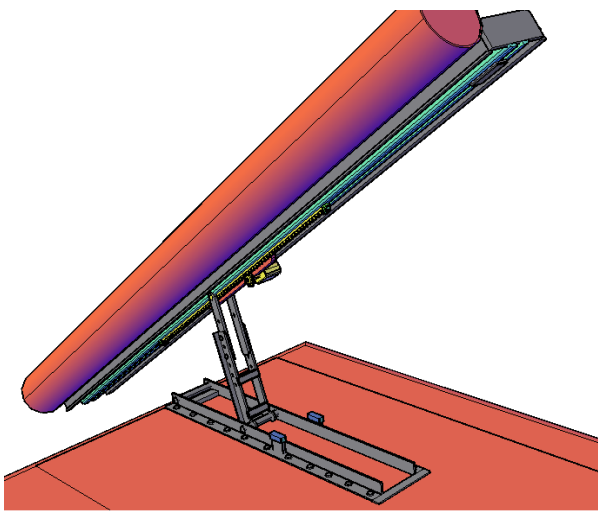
Вид устройства для спуска всасывающих рукавов и лестниц пожарной автоцистерны АЦЗ,2-40/4(43253) с установленным приводом.
